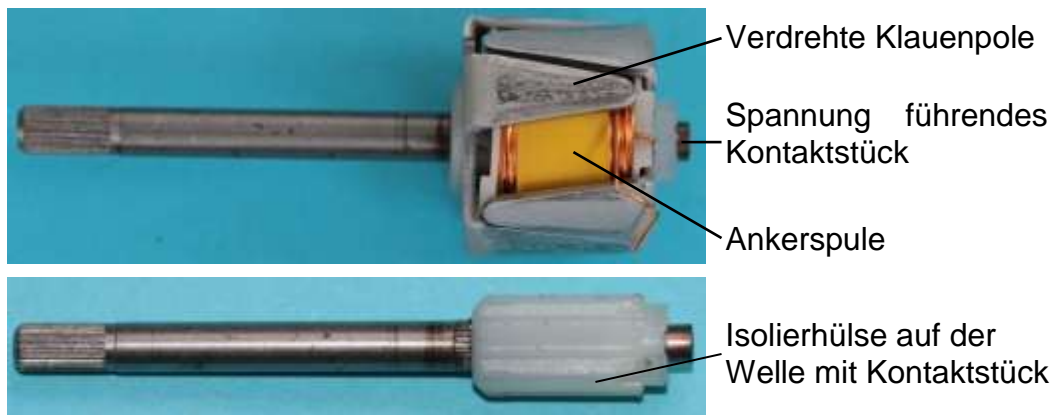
Befestigung des Klauenpolankers auf der Welle
